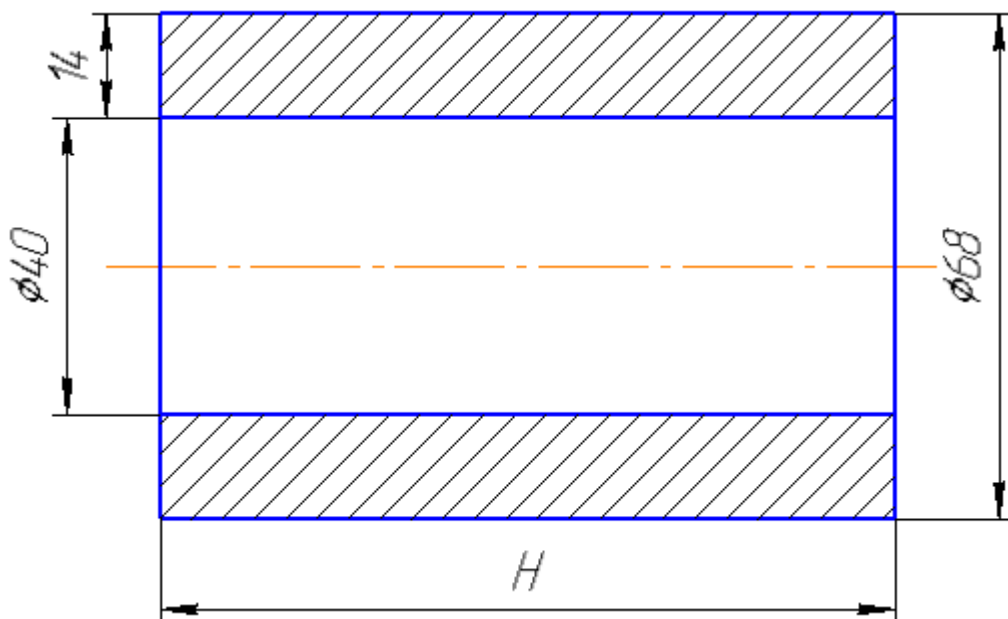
Трубна заготовка розмірами 68x14 до пресування
